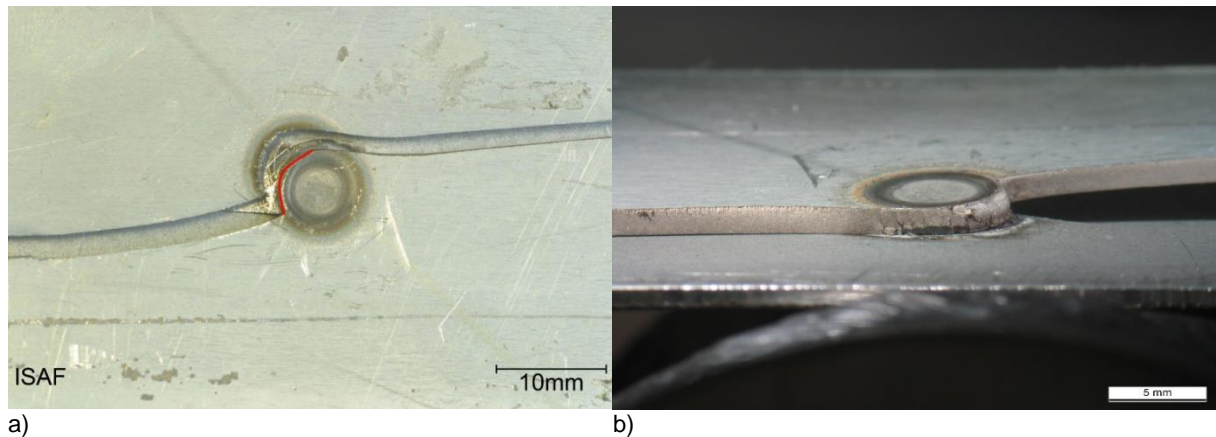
Zyklisch geprüfte FeMn1+Z/HX340LAD+Z-Punktschweißung nach Versuchsende: Draufsicht (a) und Seitenansicht (b)
